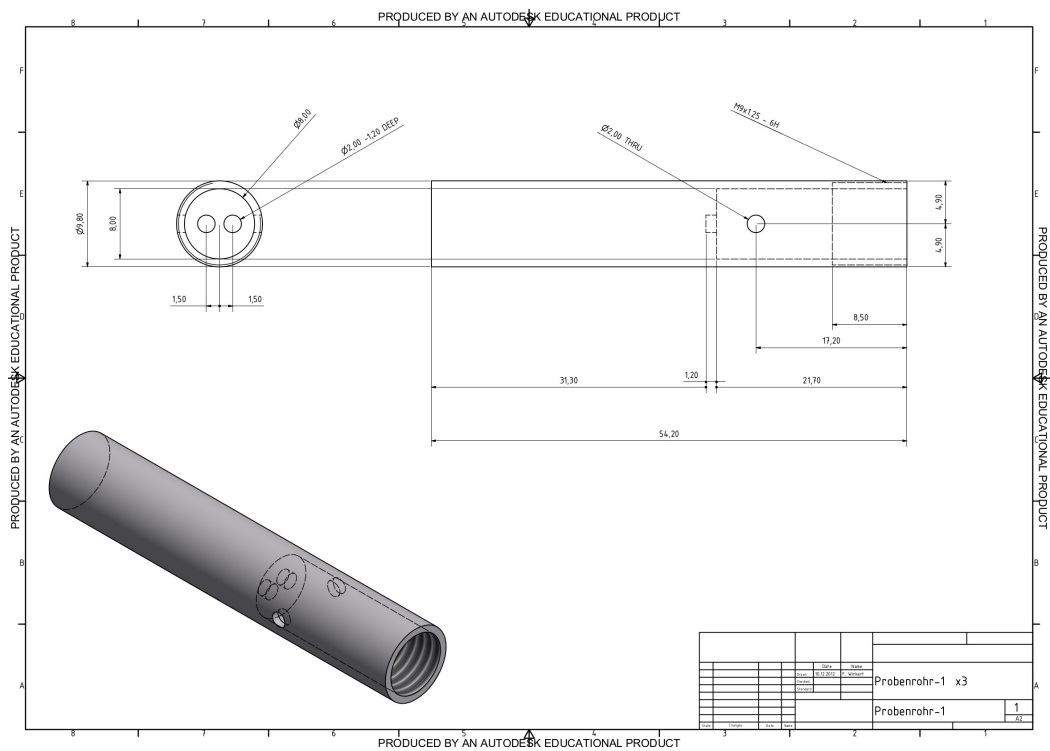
Technische Zeichnung Probenzelle 1
